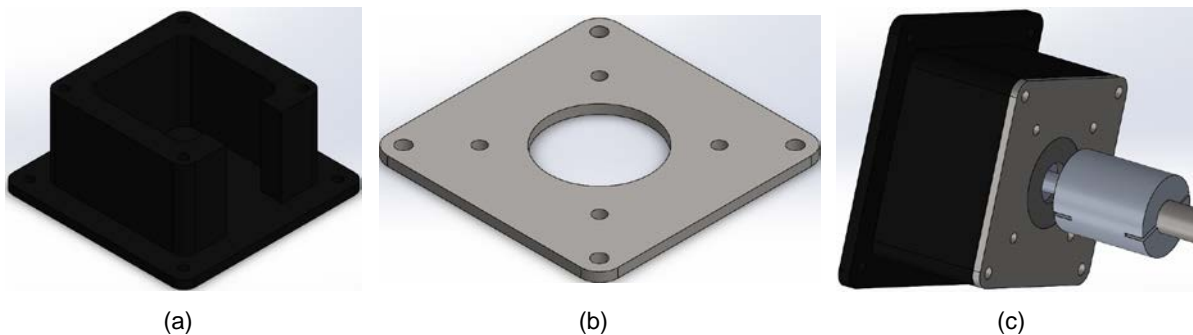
Modelo de componentes que permitem a união do motor ao fuso à plataforma de impressão.
